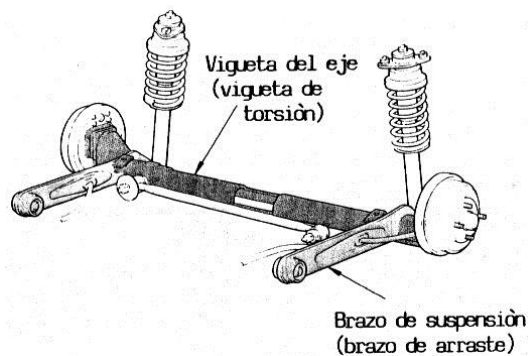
Tipo brazo de arrastre con viga de torsión.
